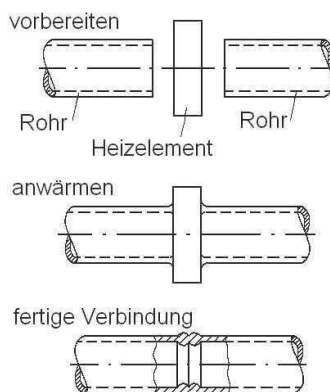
Prinzip des Heizelementstumpfschweißens am Beispiel Rohr.
